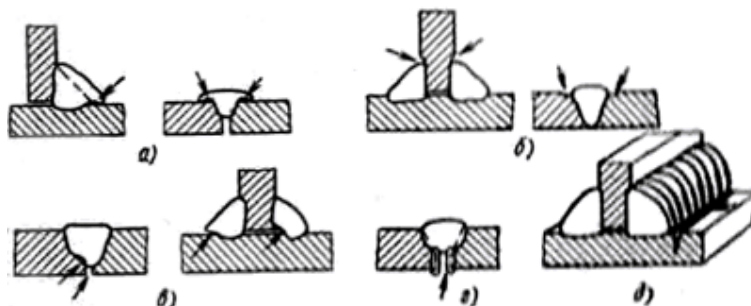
Наружные дефекты сварного шва: а – наплывы, б – подрезы, в – непровары, г – прожог, д – трещина в основном металле.
